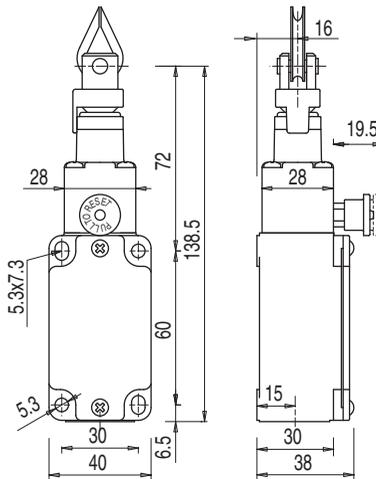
Dimensiones ERS200-MxC1x-HLR en mm
